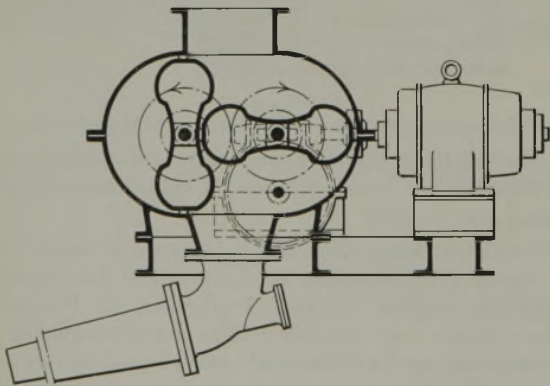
Stichlochstopfmaschine mit Drehkolben.
